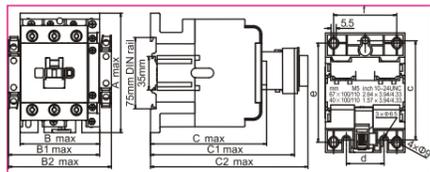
Габаритные и установочные размеры контакторов на токи 40А-95А, мм.
